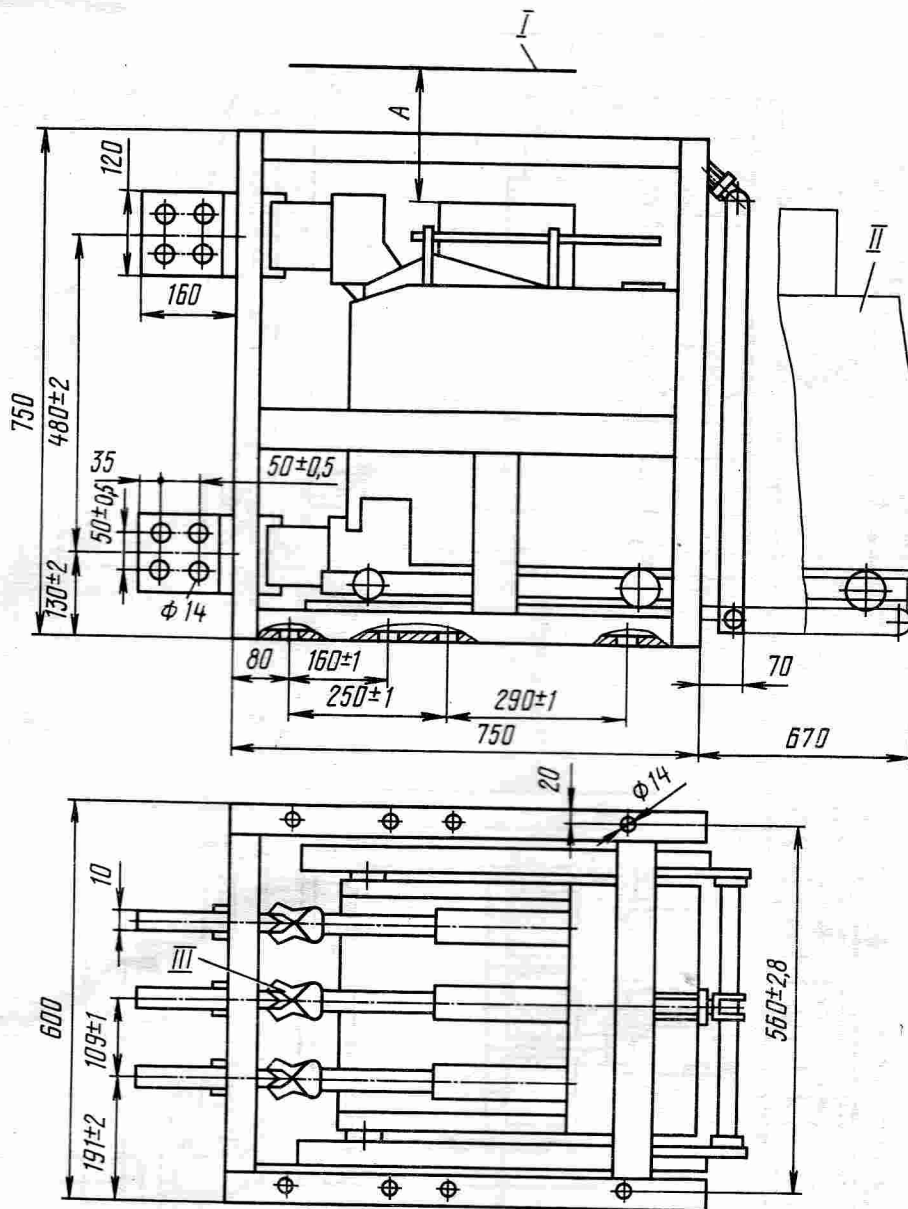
Габаритные и установочные размеры выключателей Э16В, Э25В в двух- и трехполюсном исполнении:
